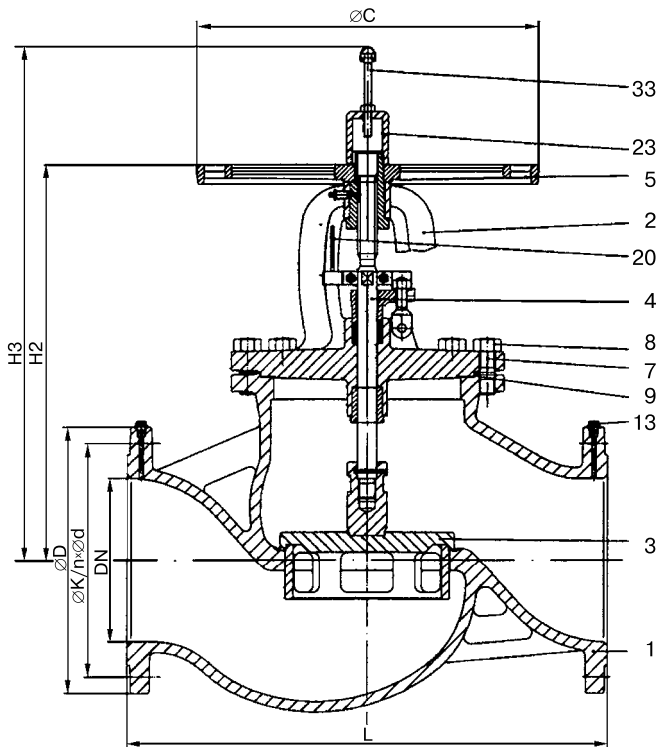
Устройство MSV-F Plus: 1 – корпус (чугун GGG-40.3); 12 – уплотнитель седла; 13 – пробка (резьба G 1/4); 2 – крышка; 3 – золотник; 4 – шпindel; 41 – силиконовый уплотнитель; 5 – маховик; 7 – шпилька; 8 – гайка; 9 – прокладка; 20 – шкала; 23 – колпак для ограничительного винта; 33 – винт блокировки настройки клапана
